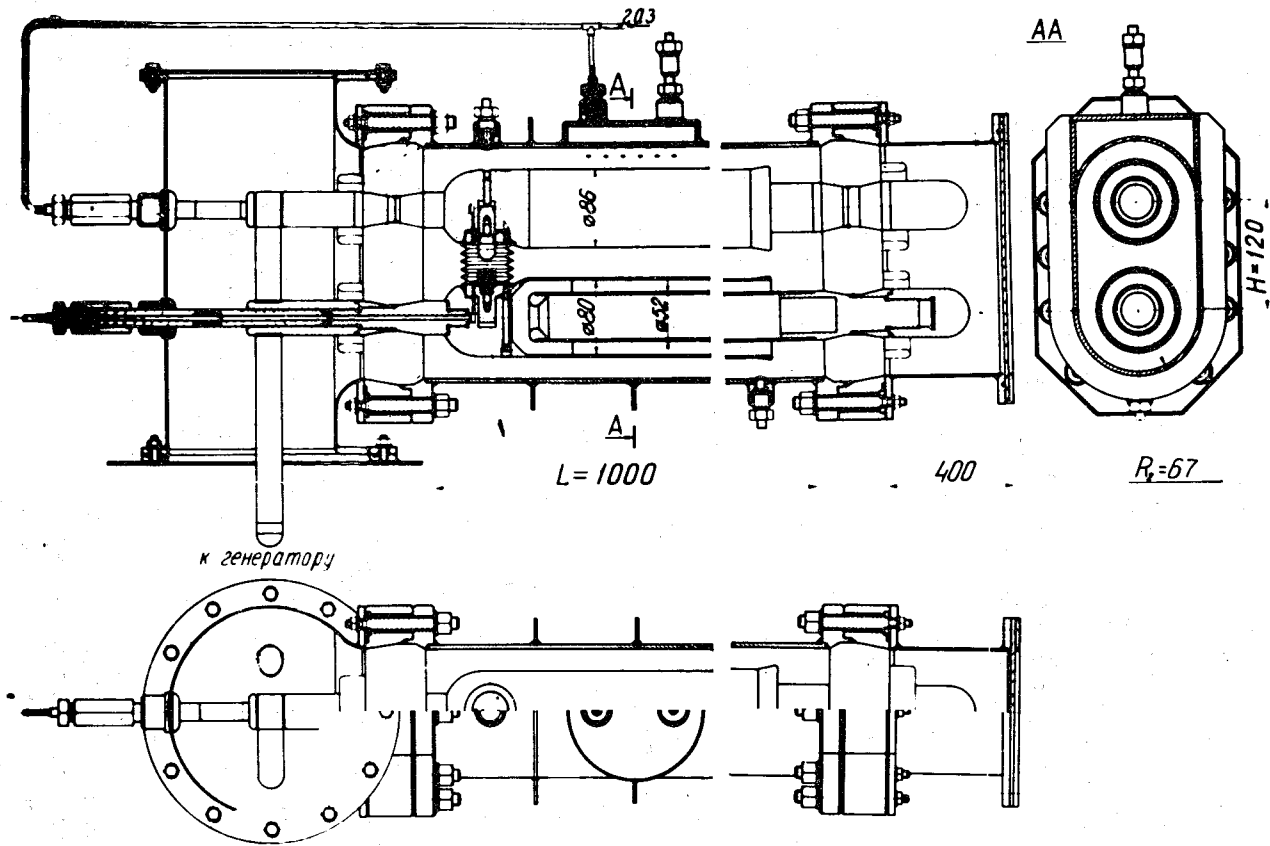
Сборочный чертеж биполярного формирователя наносекундных импульсов.
